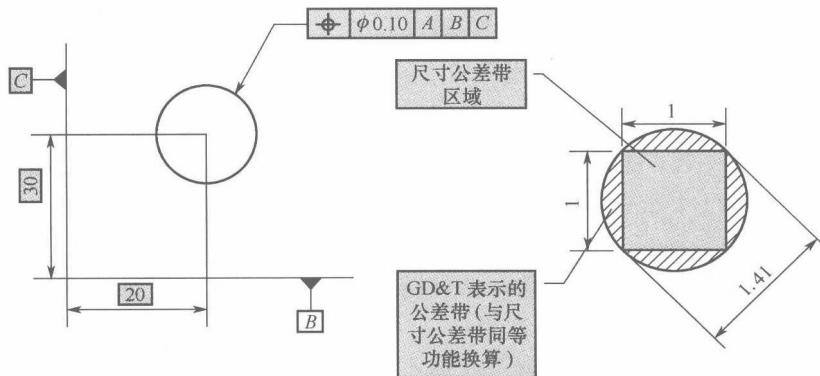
几何公差(位置度)控制的圆形公差带和尺寸公差标注控制的方形公差带的面积图示比较
